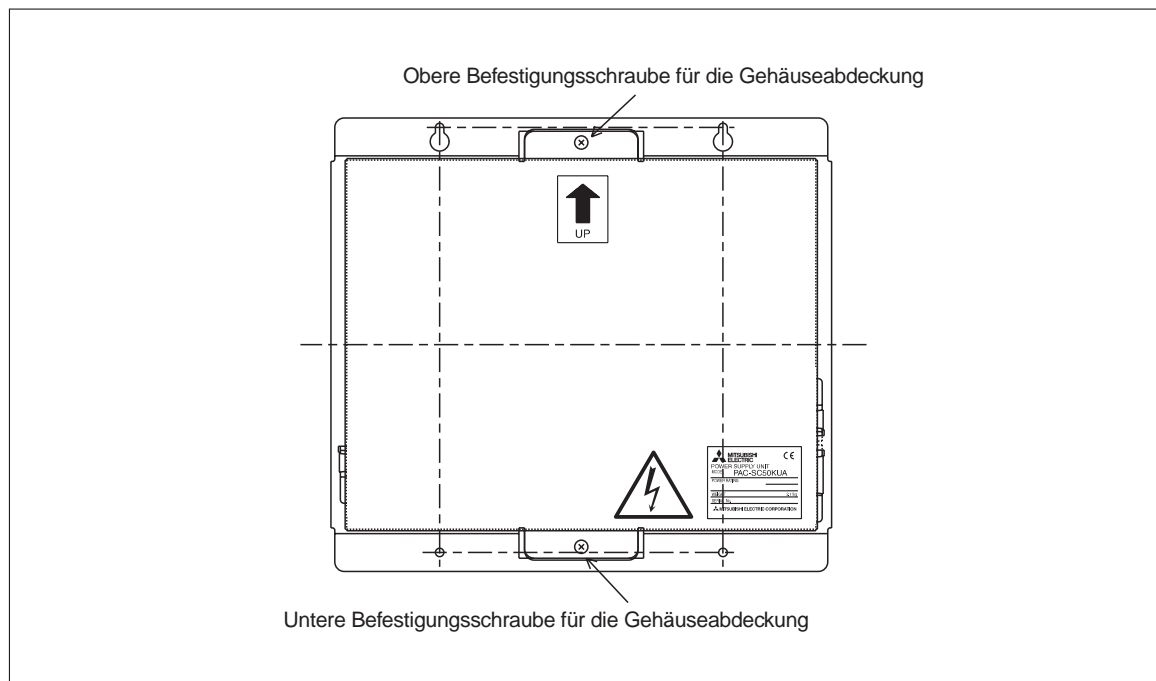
Position der Befestigungsschrauben für die Gehäuseabdeckung
